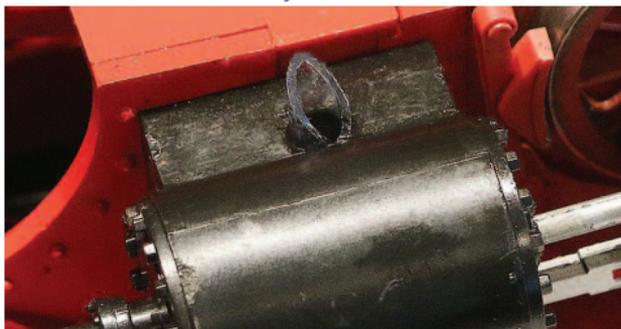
Zylinderdampfrohr mit schrägem Anschnitt.
